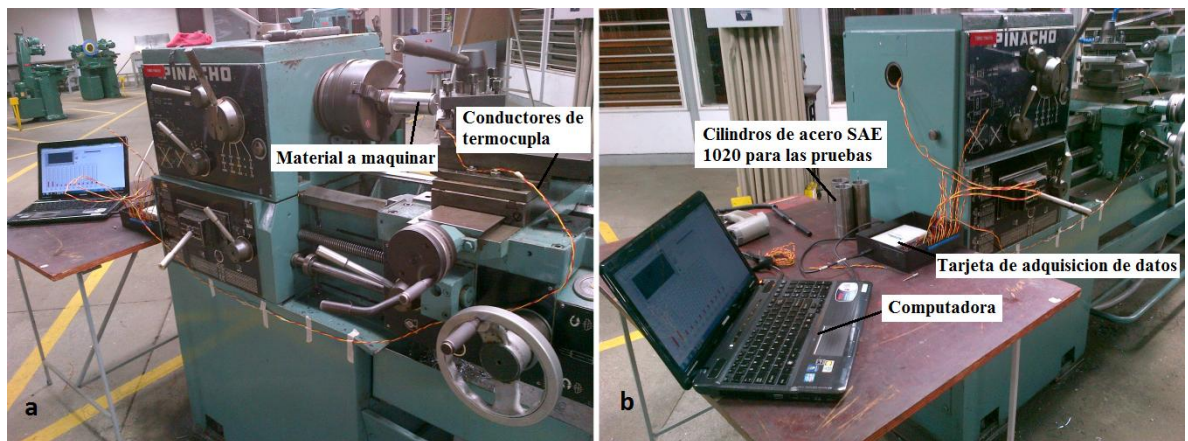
a) Vista de montaje en la herramienta, b) Vista del montaje en el computador.
